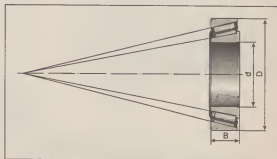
Конический роликоподшипник: d — внутренний диаметр; D — наружный диаметр; B — ширина.
